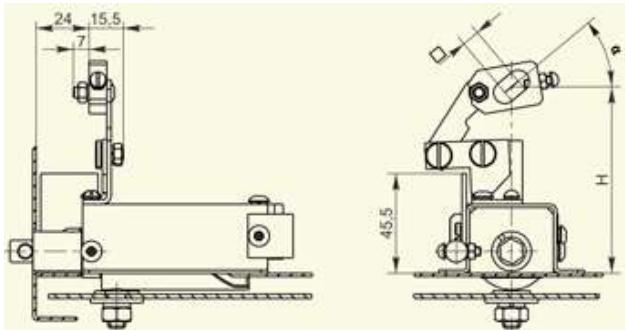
Механизм привода с узлом блокировки "Рычаг"
